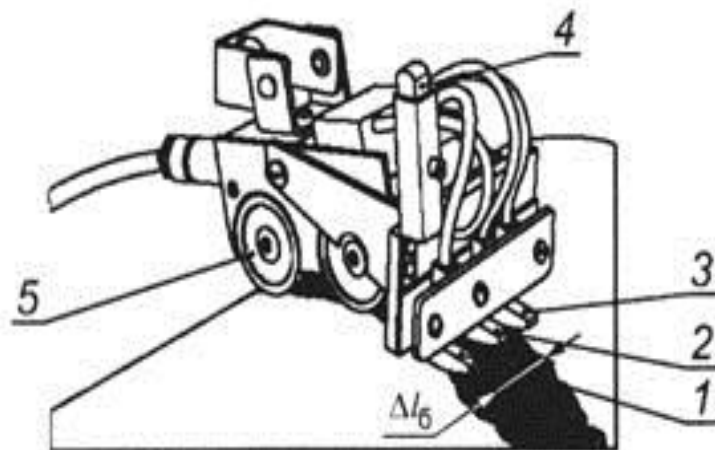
Схема контроля стыковых сварных соединений труб четырехканальным датчиком прибора ИКН-1М-4: 1, 2, 3, 4 – феррозондовые преобразователи; 5 – колеса привода измерителя длины; Δl_6 – базовое расстояние между феррозондовыми преобразователями
